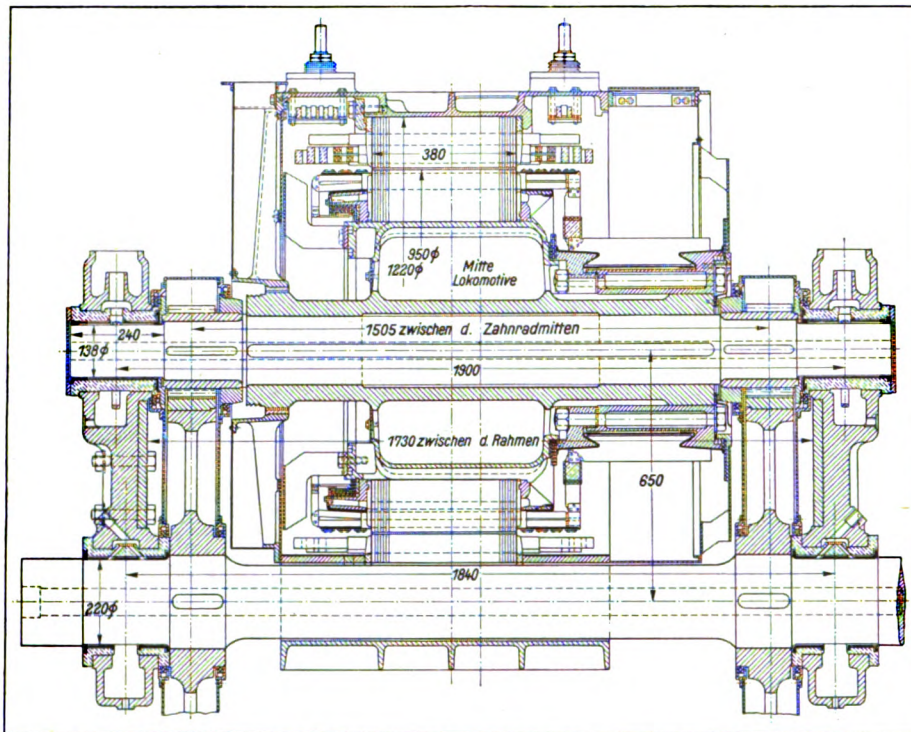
Lokomotivmotor mit zweiseitigem Zahnradantrieb.
